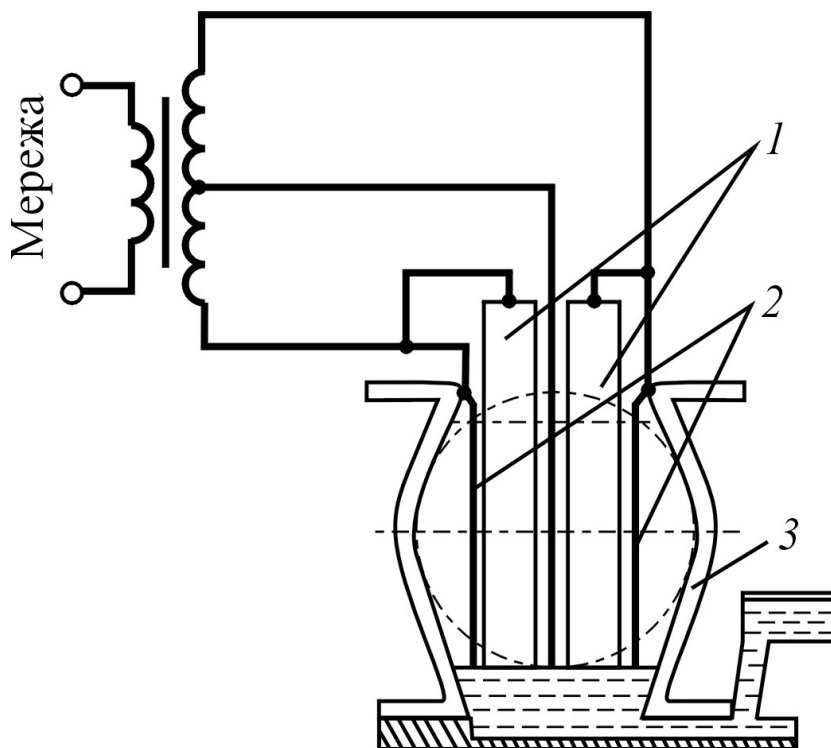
Біфілярна схема живлення установки для електрошлакового зварювання
